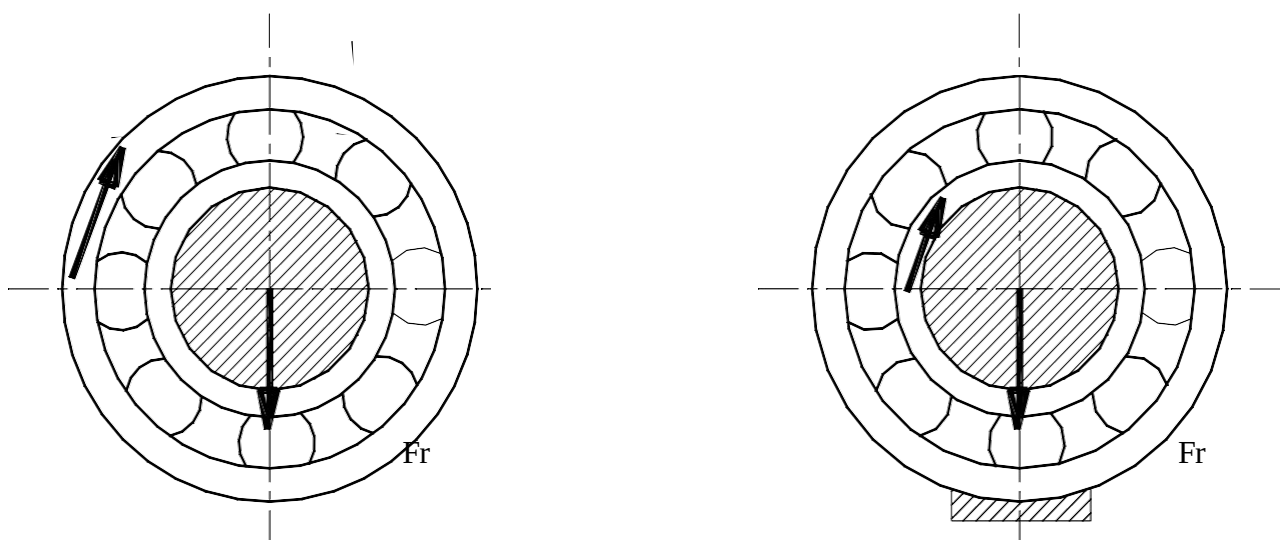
Виды нагрузок на подшипники качения: а- на наружное кольцо; б- на внутреннее кольцо.
